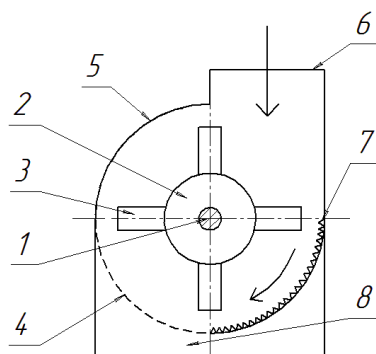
Схема молотковой дробилки: 1 – вал; 2 – молотковый ротор; 3 – молоток; 4 – решето; 5 – корпус; 6 – загрузочная горловина; 7 – дека; 8 – выгрузная горловина
